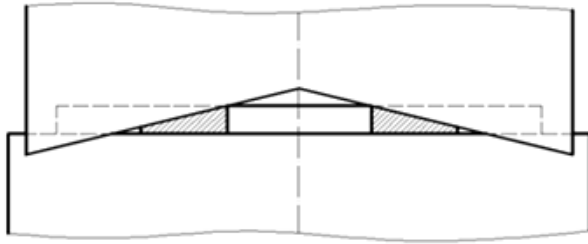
Конструкція ножиць для поперечного розрізання плоского металопрокату з нижнім рухомим похилим ножом («НКМЗ», м. Краматорськ, Україна)
